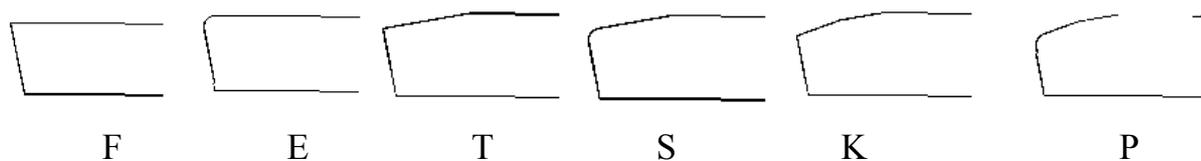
Формы режущей кромки неперетачиваемых пластин
